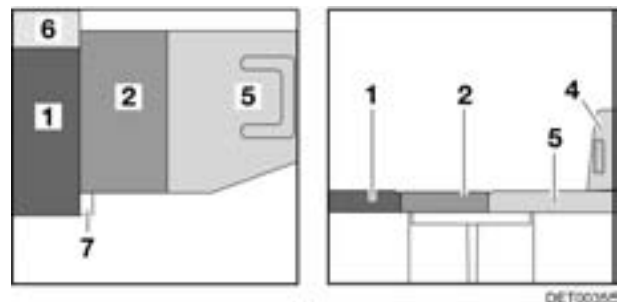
Nach dem Umbau (mit Sitzverbreiterung)
